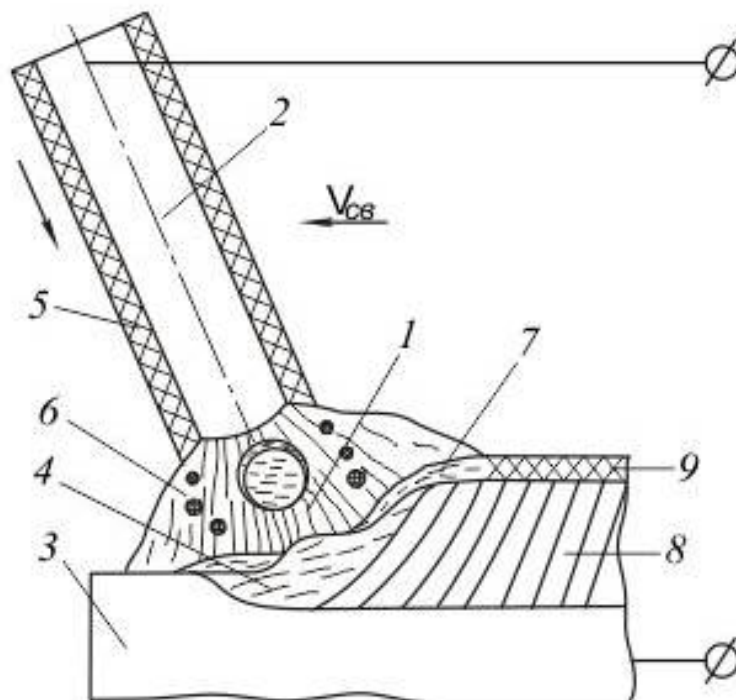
Схема процесса ручной дуговой сварки
